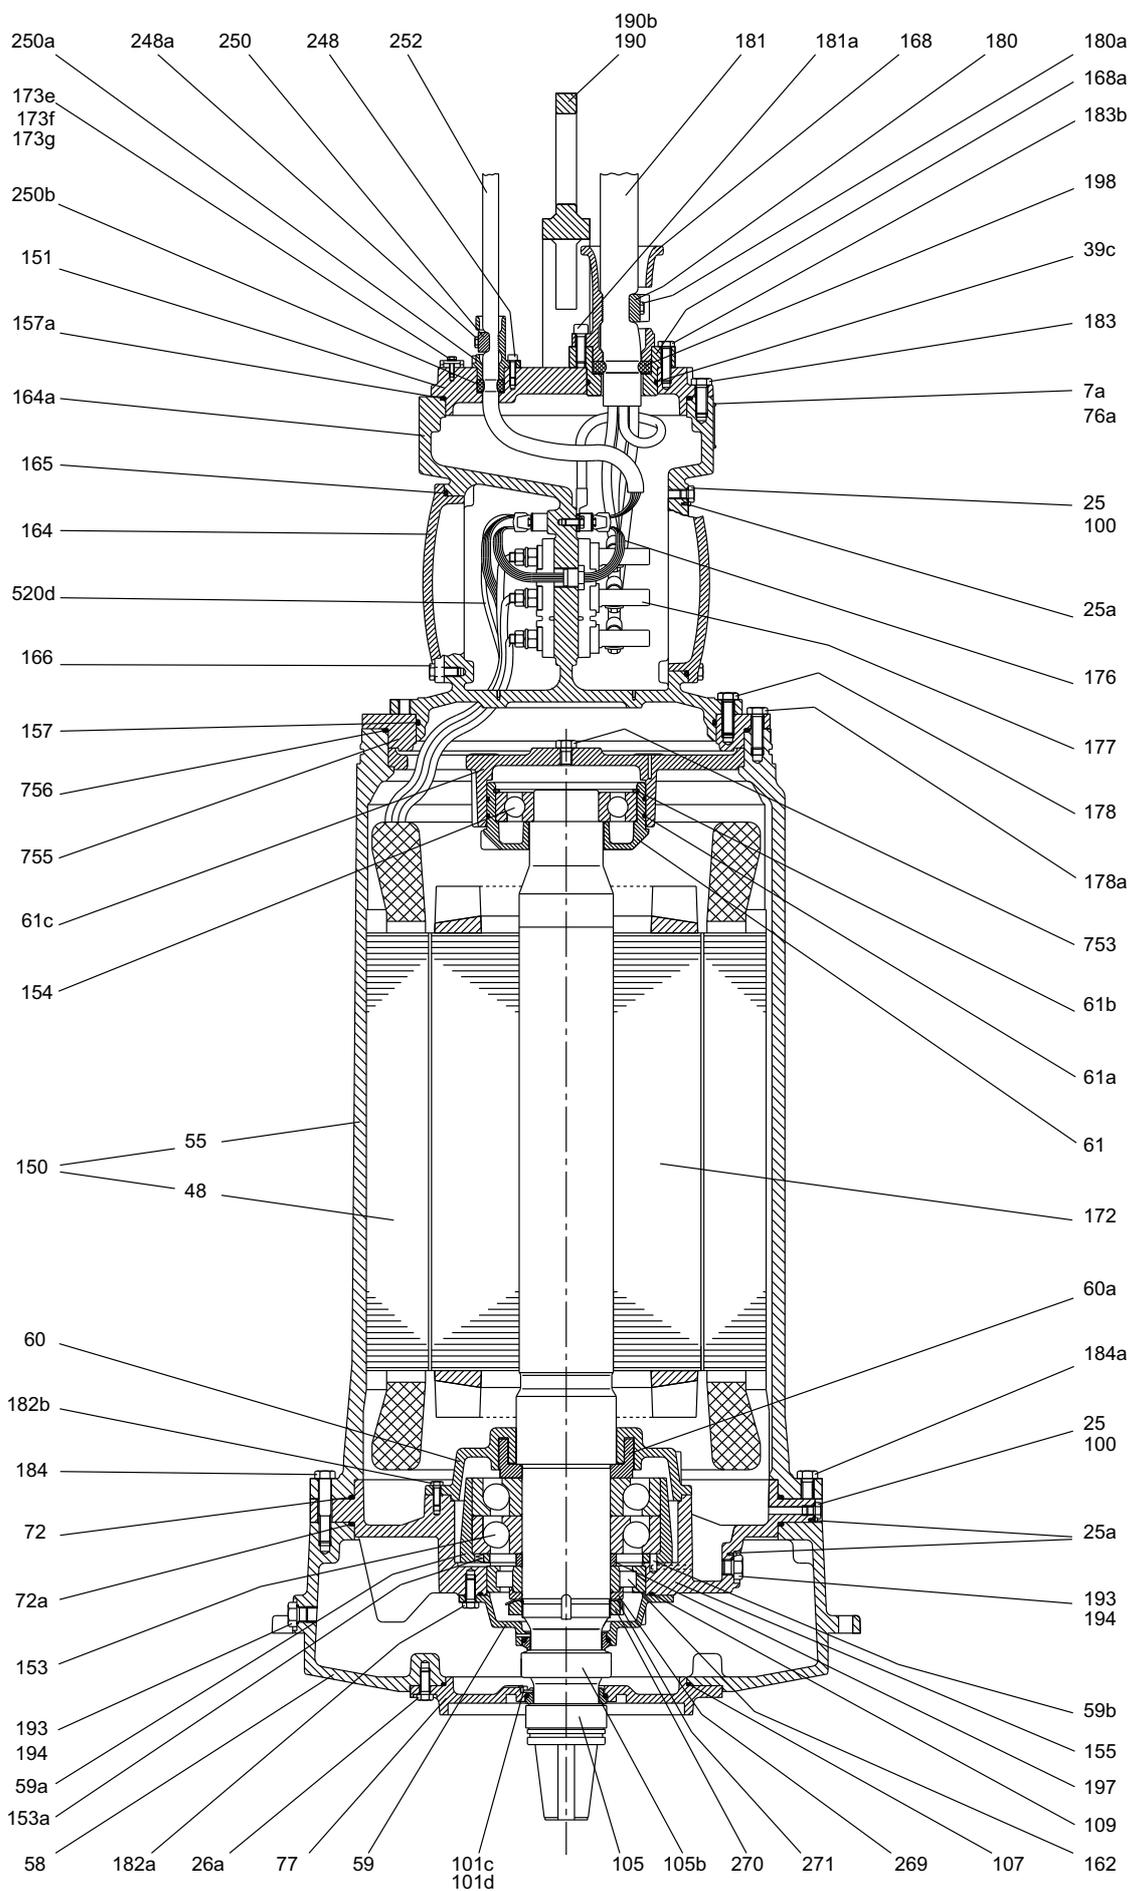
Взрывозащищённый электродвигатель, установка в обсадной трубе (ST)
